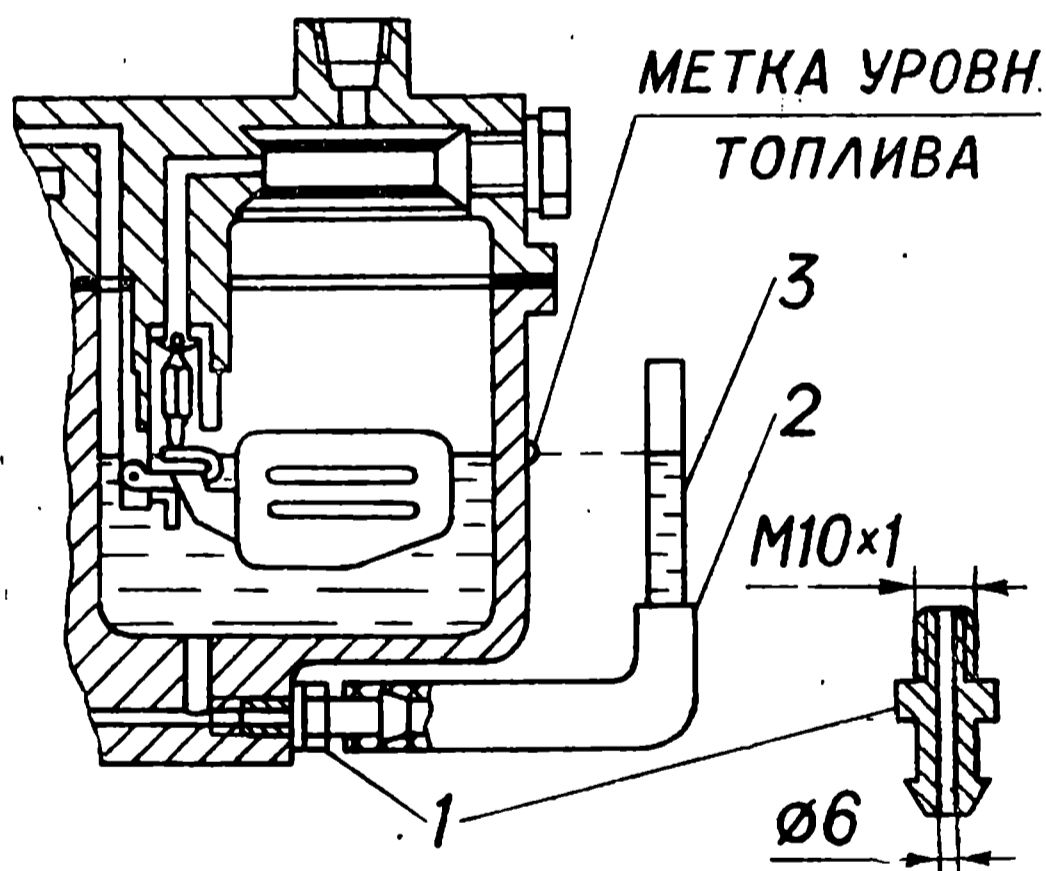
Схема проверки уровня топлива в поплавковой камере:
